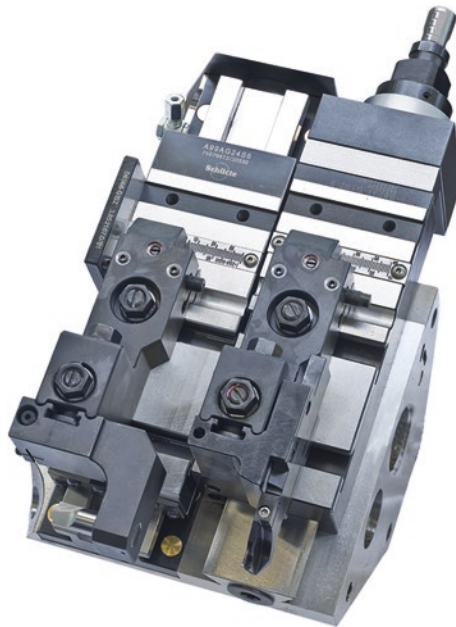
Doppelquerschlitten einer Kurvenmaschine mit Abstecherschlitten (rechts) und rückwärtigem Bearbeitungswerkzeug (links) [Schu08]
